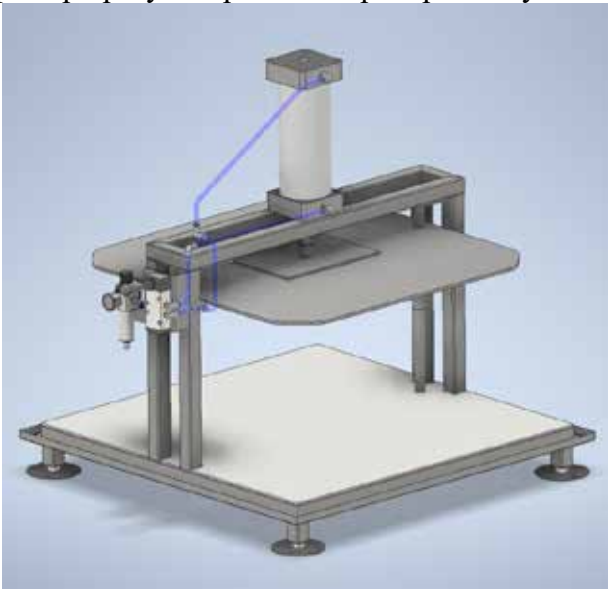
Загальний зовнішній вигляд пневматичного преса, з піднятою полицкою
